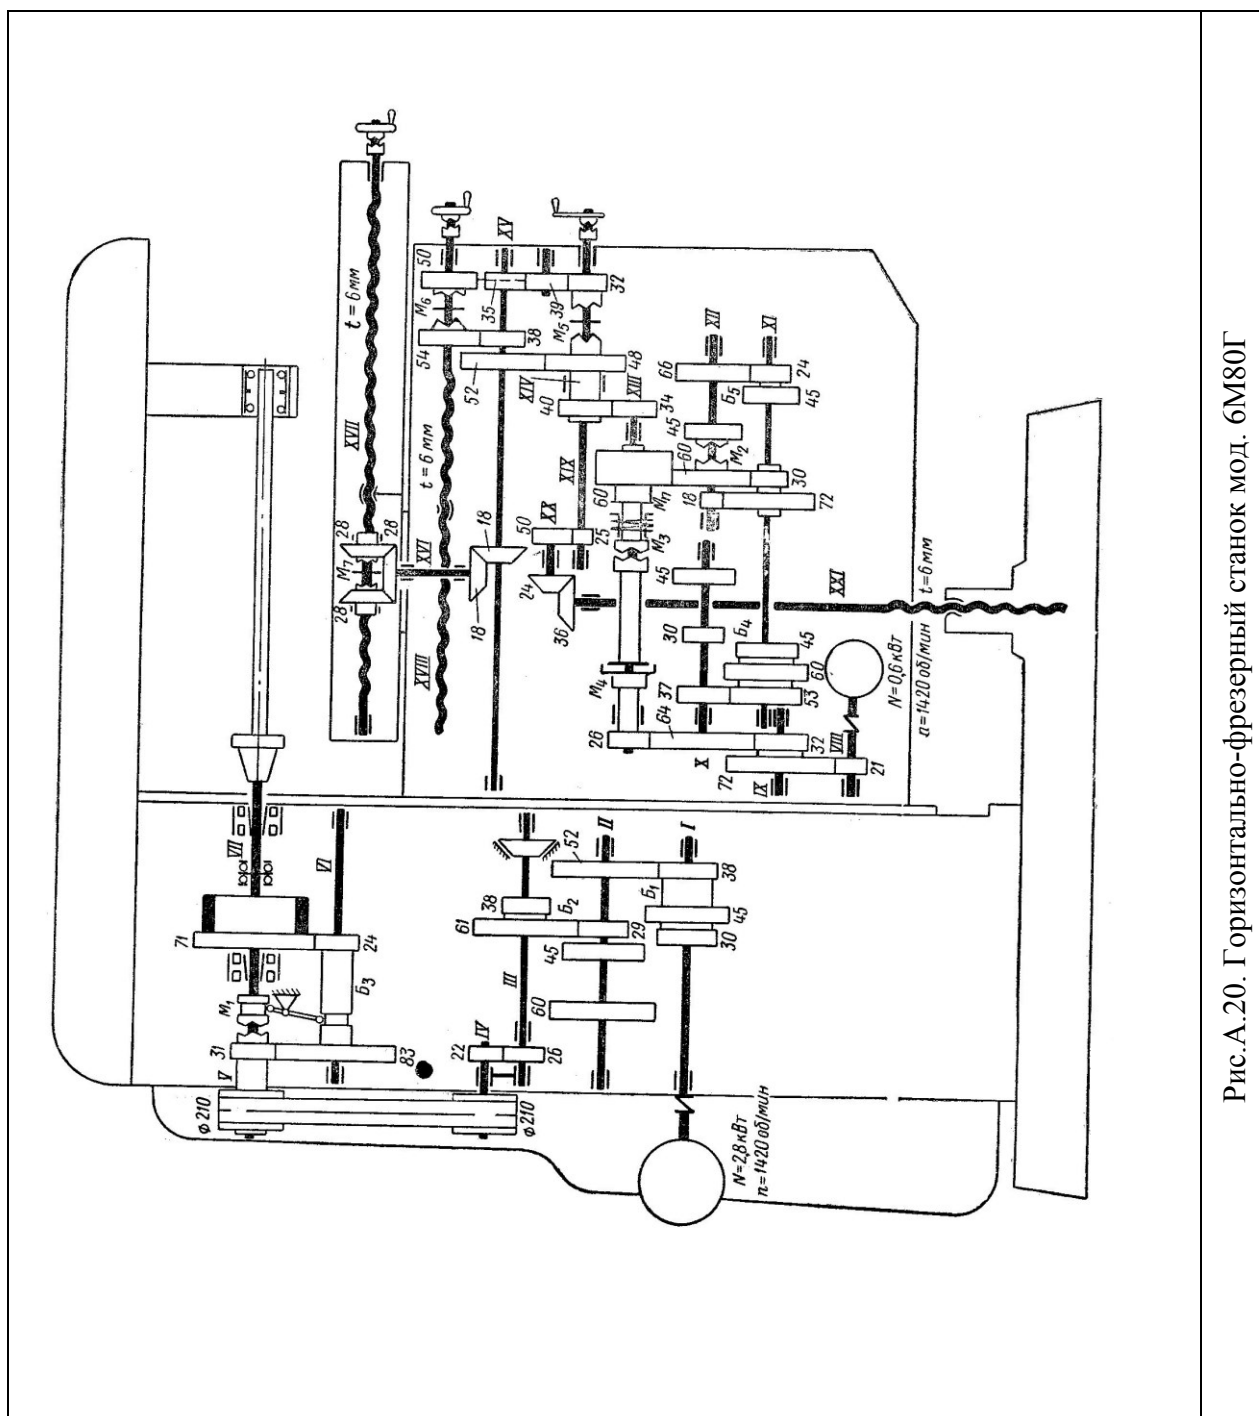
Горизонтально-фрезерный станок мод. 6М80Г
